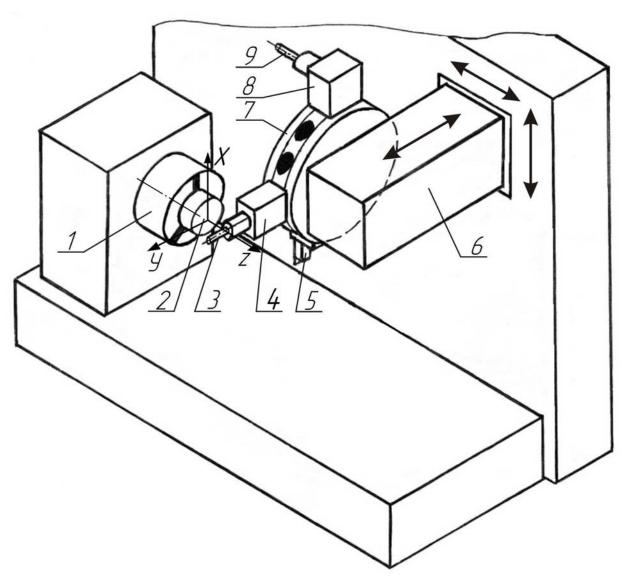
Структурная схема токарно-фрезерного многофункционального центра: I — шпиндель; 2 — деталь; 3, 9 — фрезы; 4 — фрезерный блок обработки детали в плане Y-Z; 5 — токарный резец; 6 — элемент крепления инструментального магазина; 7 — инструментальный магазин типа «револьверная головка»; 8 — фрезерный блок обработки детали в плане X-Y
